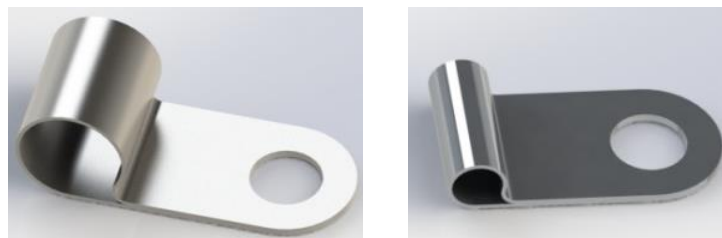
Abrazaderas para cableado del driver (Fuente: propia)
